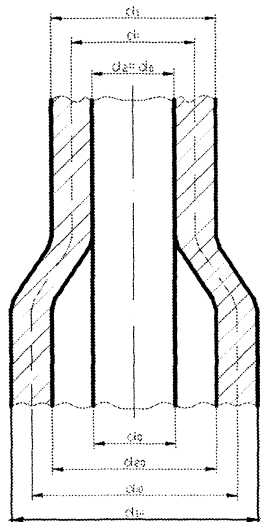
Схема пластической деформации трубной заготовки взрывом
